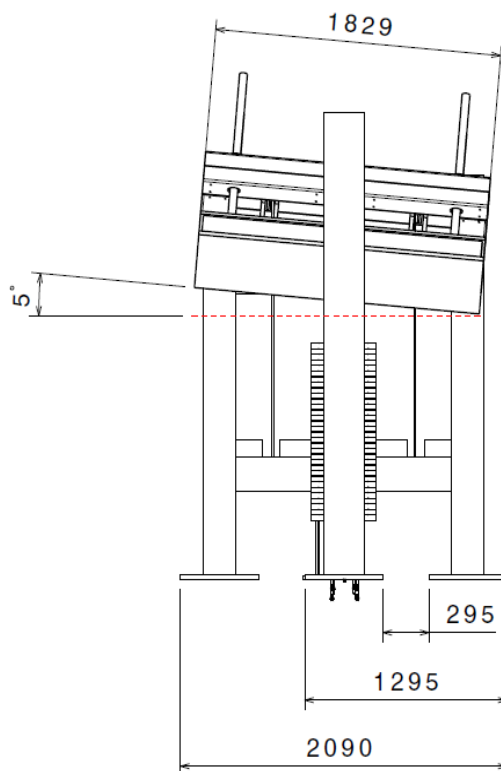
Vista lateral esquerda da versão final do dispositivo Roof Crush.
